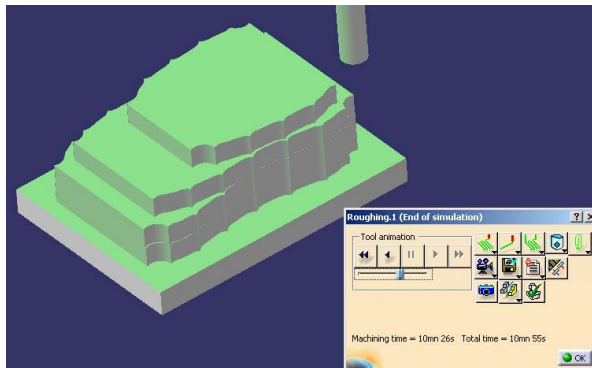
Definování jednotlivých prvků pro obrábění nahrubo a sladění počátku souřadnicového systému CAD/CAM se souřadnicovým systémem stroje
